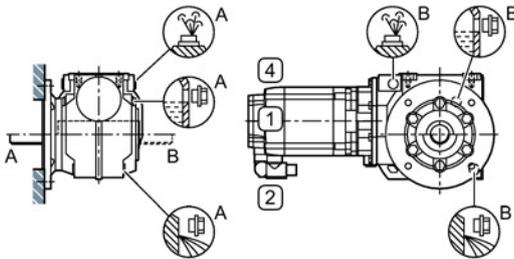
Einbaulagen für Stirnradschneckengetriebe CF (Flansch-) und CAZ (Gehäuseflanschausführung), Baugröße 29, 2-stufig
